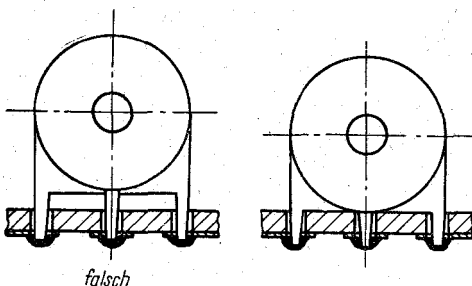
Montage eines Potentiometers mit drei Haltelappen
